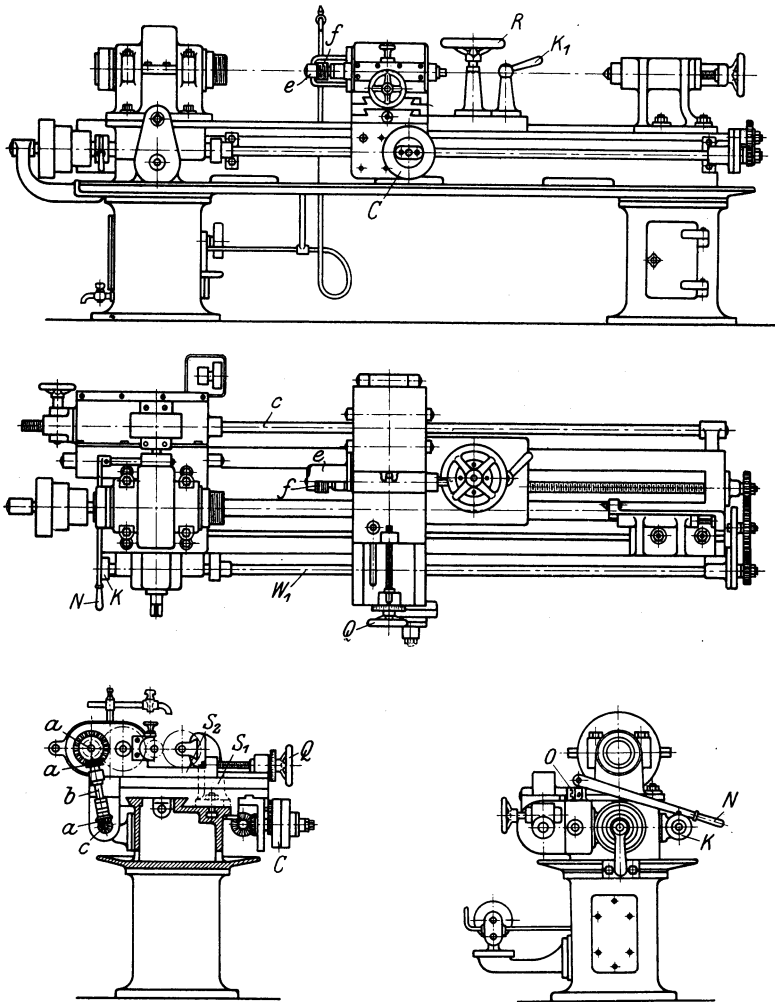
Die Gewindefräsmaschine von Schilling und Krämer.
